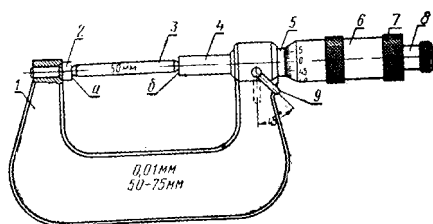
Микрометр для наружных измерений: 1 – скоба; 2 – жесткая пятка; 3 – калибр (концевая мера) для установки микрометра на нуль; 4 – подвижная пятка (микровинт); 5 – стержень; 6 – микрометрическая головка; 7 – установочный колпачок; 8 – трещоточное устройство; 9 – тормозной приспособление
